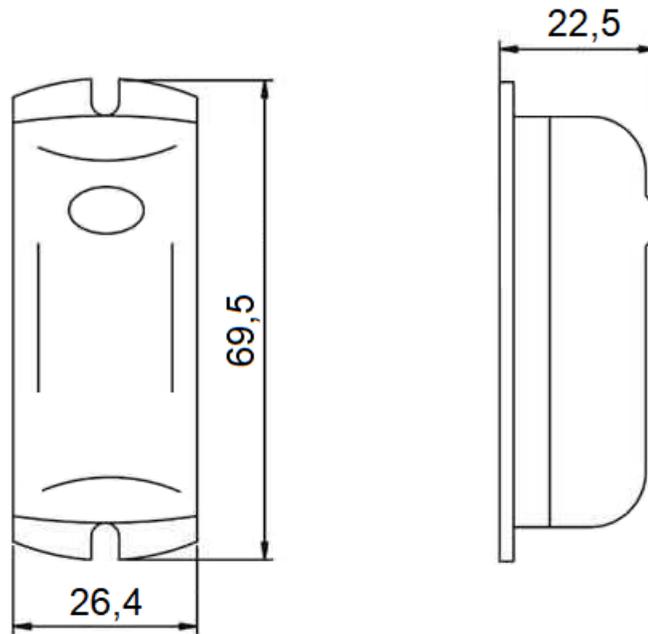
Габаритные размеры излучателя и приемника
